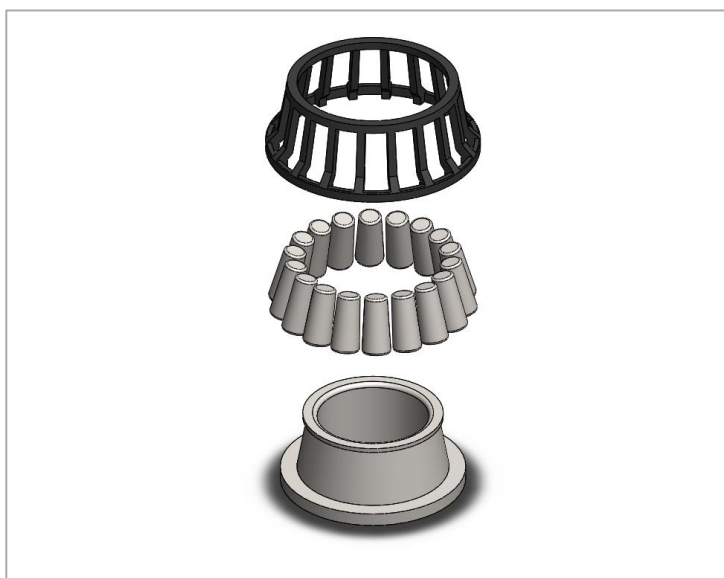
117 Explosionado rodamiento cónico primario marcha atrás
